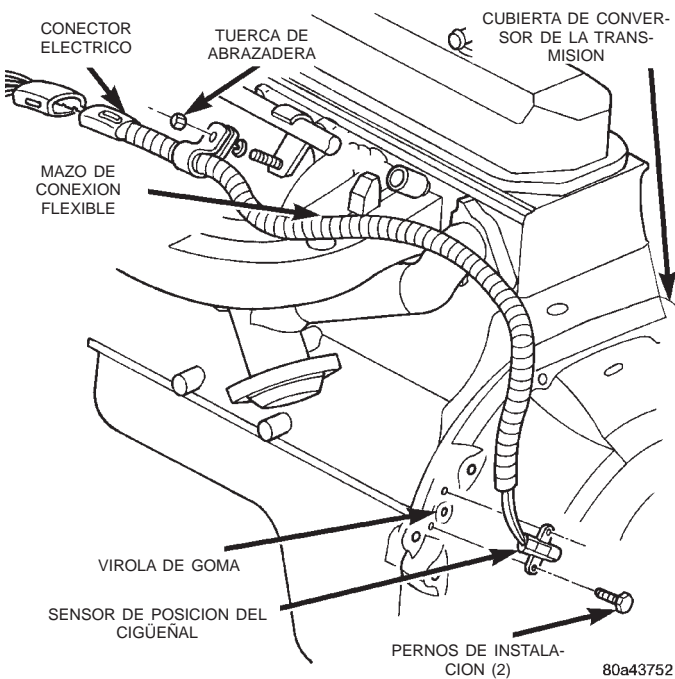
Sensor de posición del cigüeñal —Motor 4.0L
